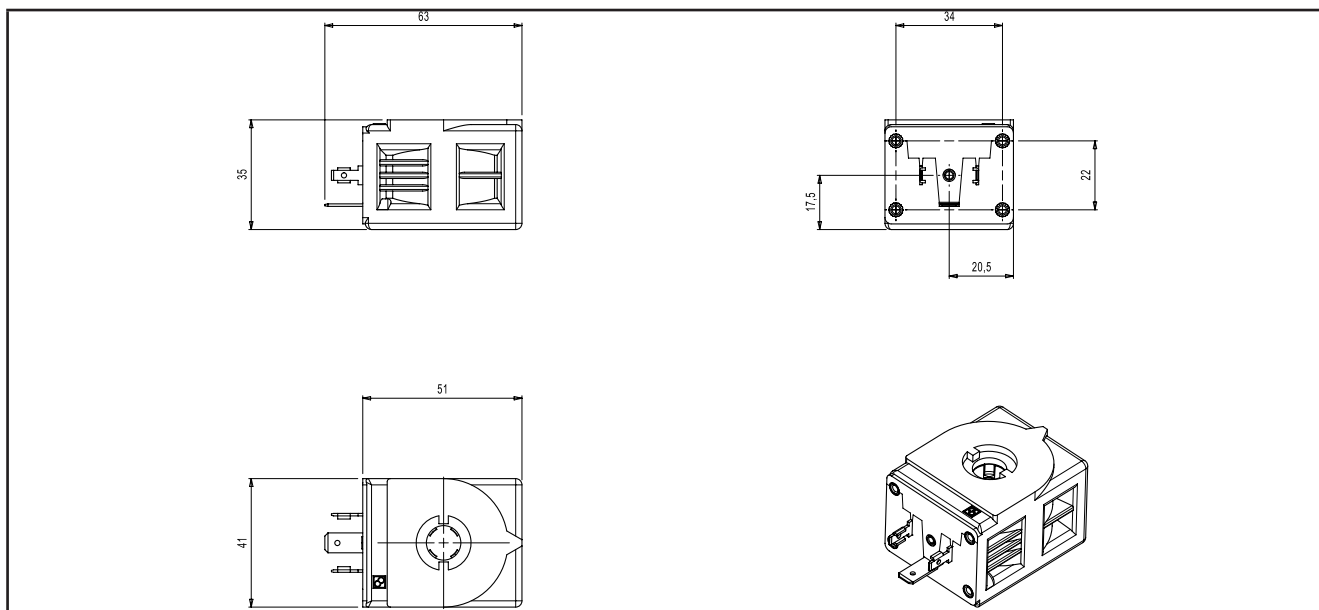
Dimensioni meccaniche bobina modelli PXVB0ARA60100, PXVB0ARA20100
